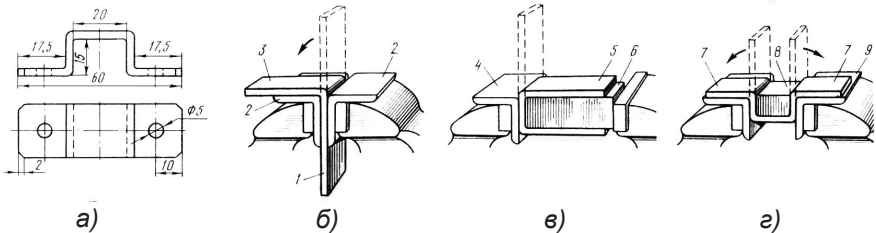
Гибка прямоугольной скобы: а) чертеж для определения длины скобы, б, в) гибка одного и другого конца скобы, г) формирование скобы; 1 - заготовка, 2 - нагубники, 3, 5 - концы скобы, 4, 9 - нагубники, 6, 8 - большой и малый бруски оправки, 7 - лапки
